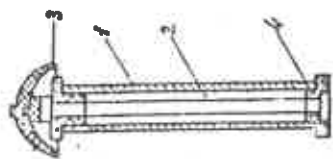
1-țevă; 2-tub PVC din; 3-ospac de fixare și protecție; 4-bucă de fixare a tubului PVC.
